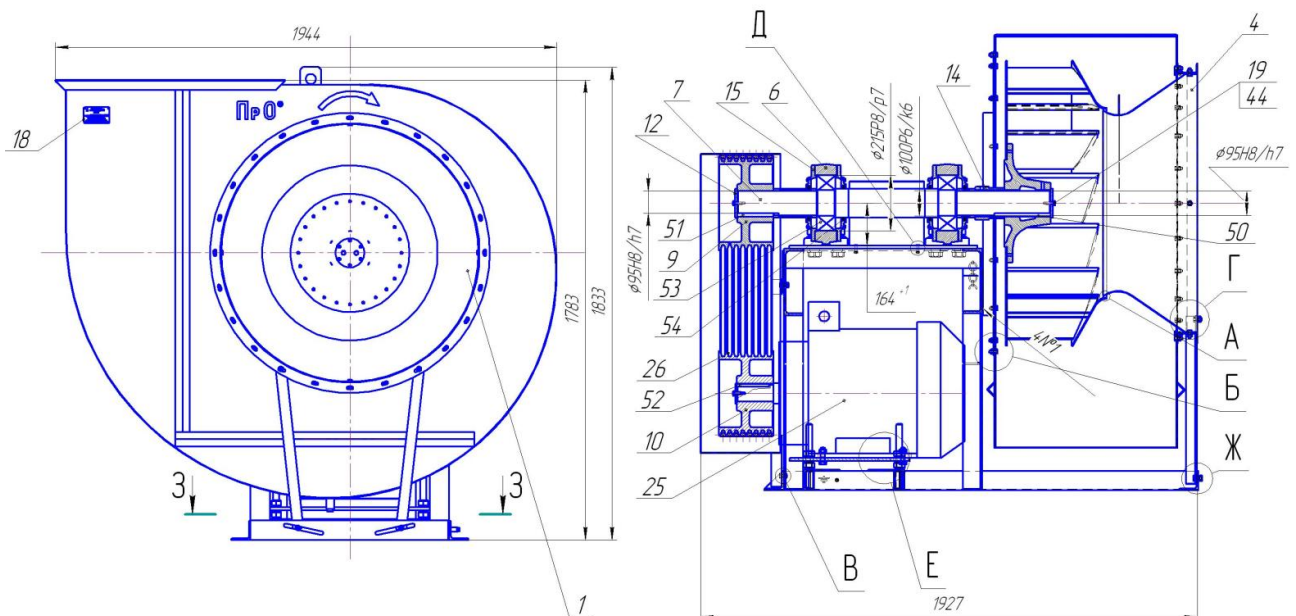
Складові частини, габаритні і основні приєднувальні розміри вентилятора В-Ц4-76-10Ж-02: 1 – станина; 2 – корпус; 3 – розтруб; 4 – колесо; 5 – вузол вала; 6 – двигун; 7 – огороження.
